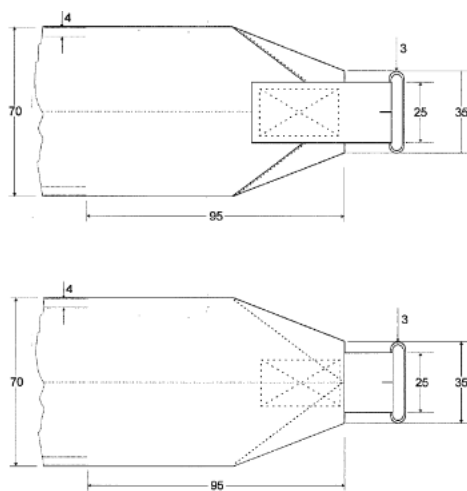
Vista da correia de fixação do suporte metálico (medidas em mm)
